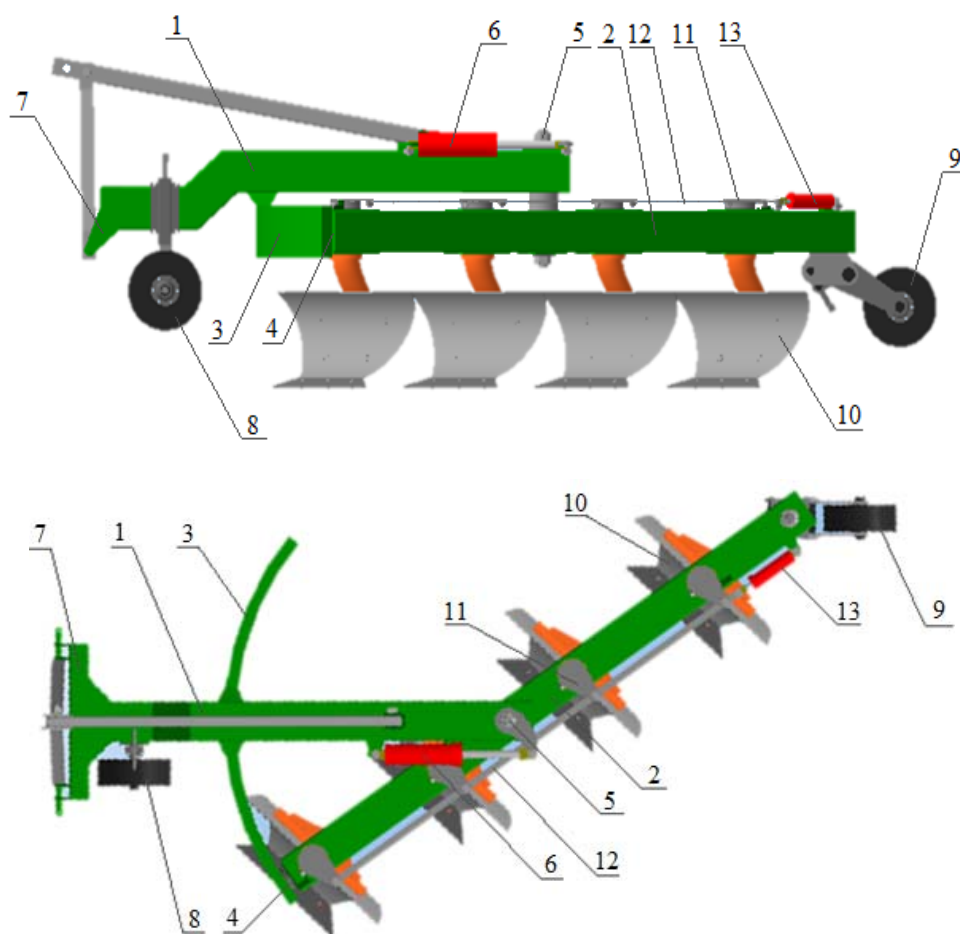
Схема поворотного плуга для гладкой вспашки
